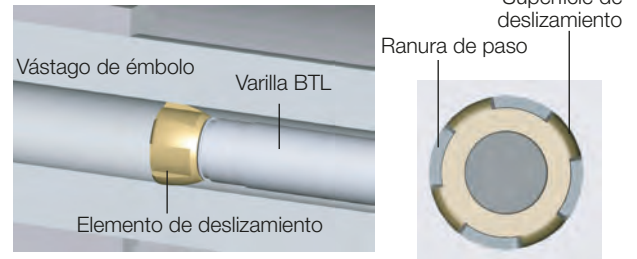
Vista detallada y vista desde arriba del elemento de deslizamiento
